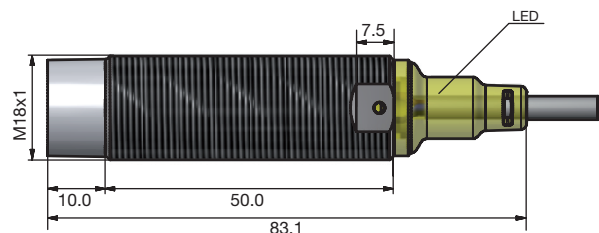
Lange Ausführung, Nicht bündiger Einbau, Kabel
